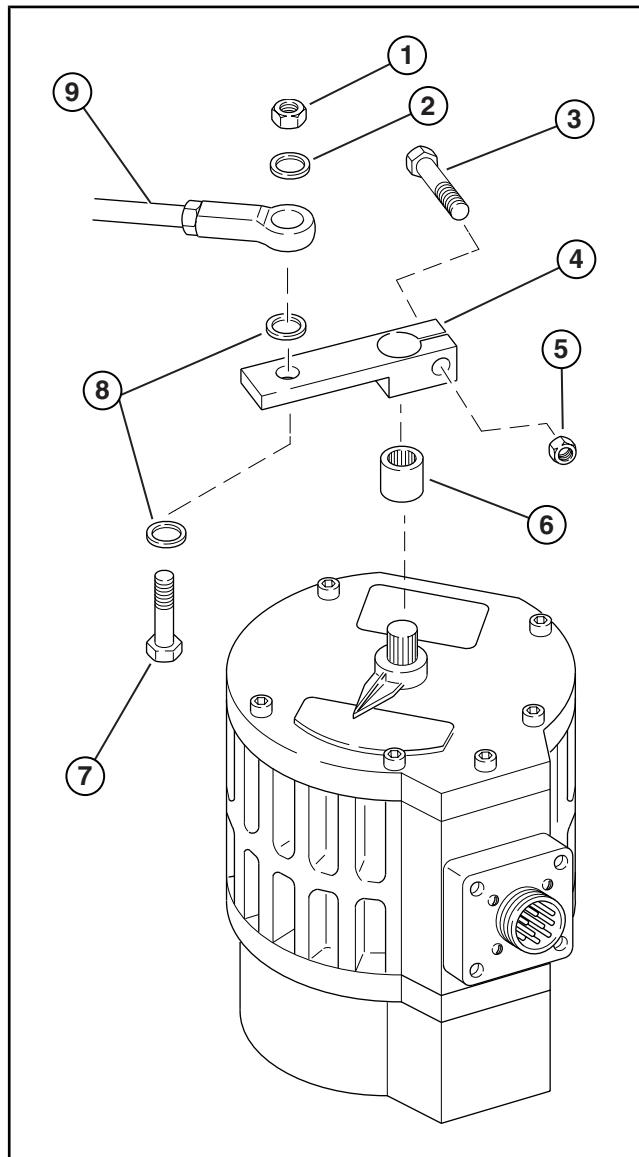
Рычажный механизм регулятора оборотов
